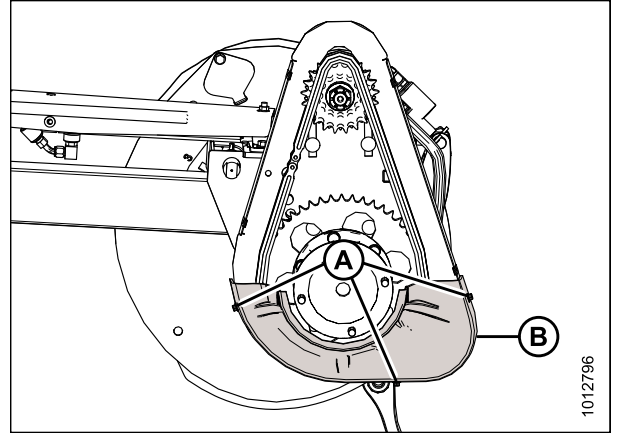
Cubierta de mando inferior (cubierta superior retirada)
